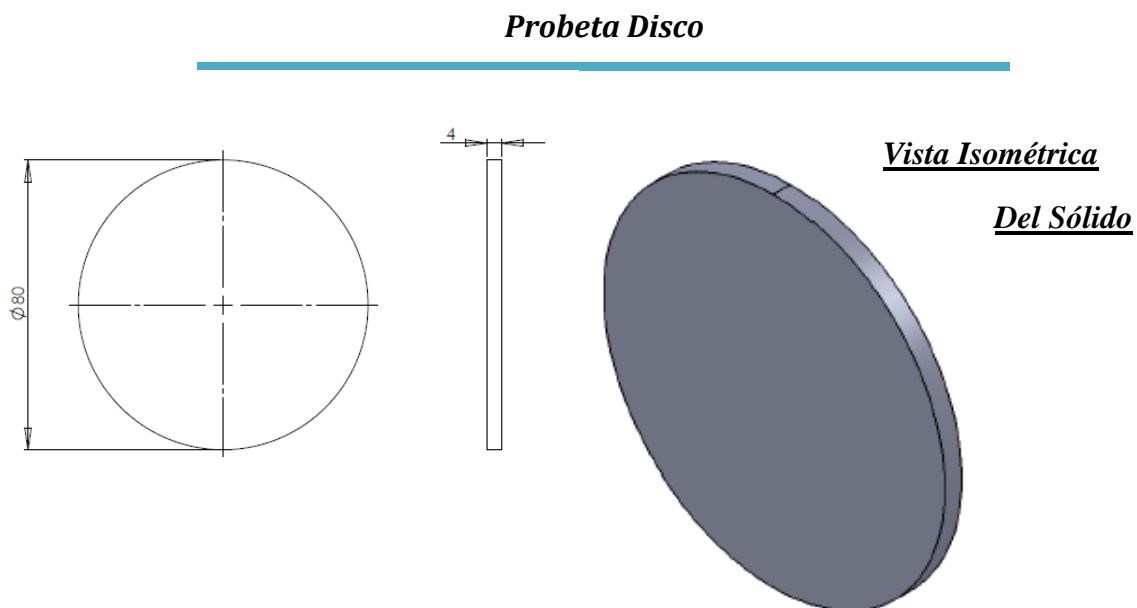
Dimensiones y Geometría de la Probeta de Disco (cotas en mm)
